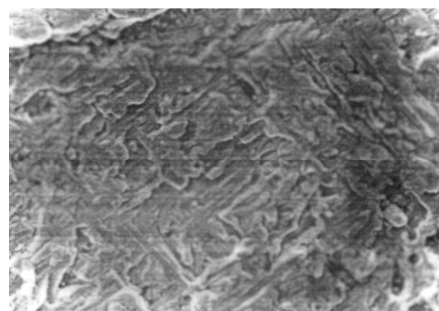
Фракторамма излома рычага из титанового сплава BT22 в очаге зарождения усталостной трещины; $\times 800$.
